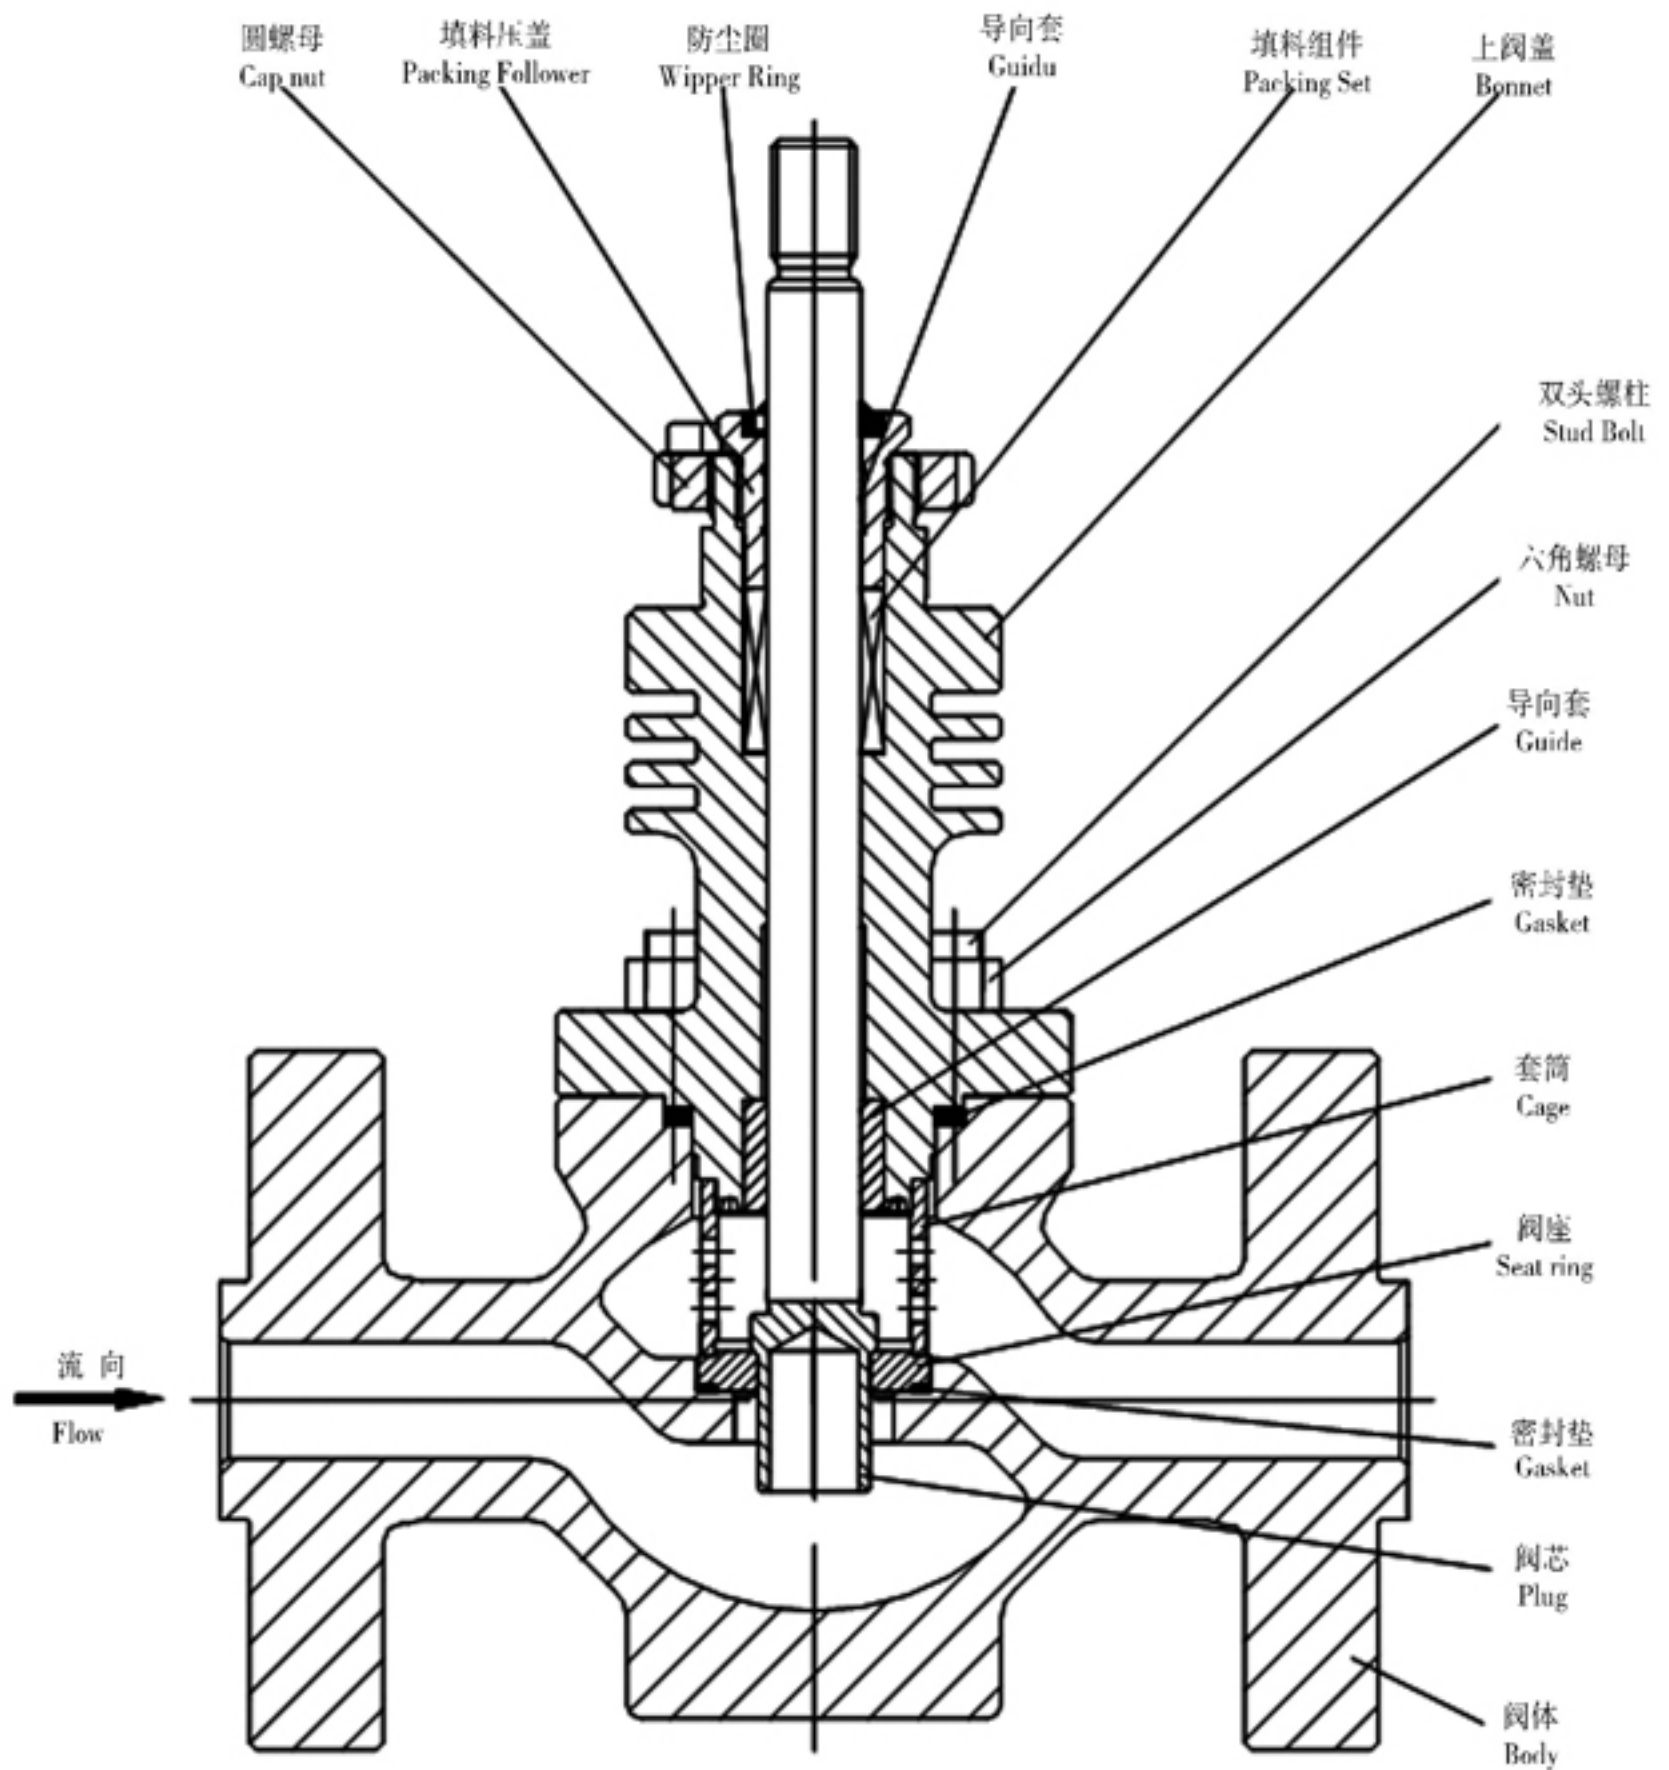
本体部构造 Fig.3 BODY SECTION VIEW
